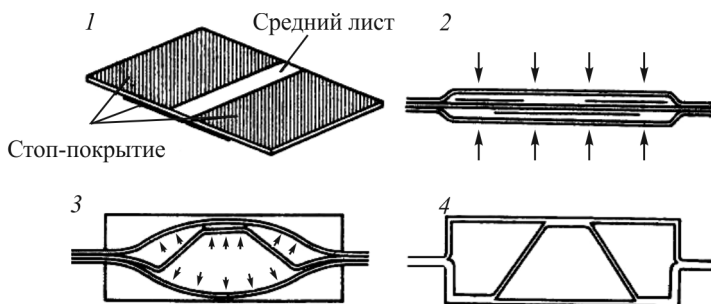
Схема получения многослойной панели методом совмещения диффузионной сварки с формообразованием: 1 – подготовка к сварке; 2 – сварка пакета; 3 – формование панели; 4 – окончательная форма детали
